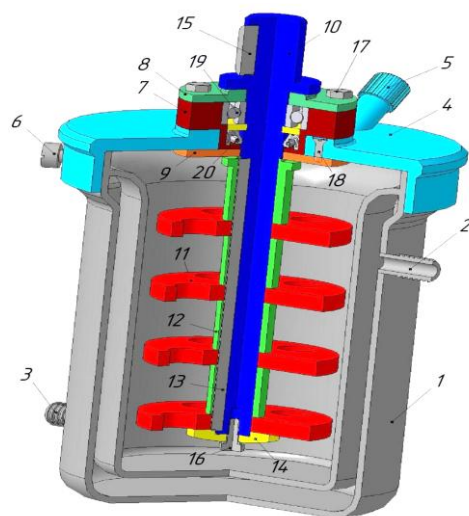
Схема робочої камери лабораторного бісерного млина вертикального типу: 1 — стакан; 2, 3 — патрубки для охолоджувальної рідини; 4 — кришка; 5 — пробовідбірник; 6 — фіксатор кришки; 7 — підшипниковий вузол; 8 — кришка; 9 — шайба; 10 — вал; 11 — диск; 12 — втулка; 13 — шпонка; 14 — шайба; 15 — шпонка; 16, 17, 18 — гвинти; 19 — підшипник
